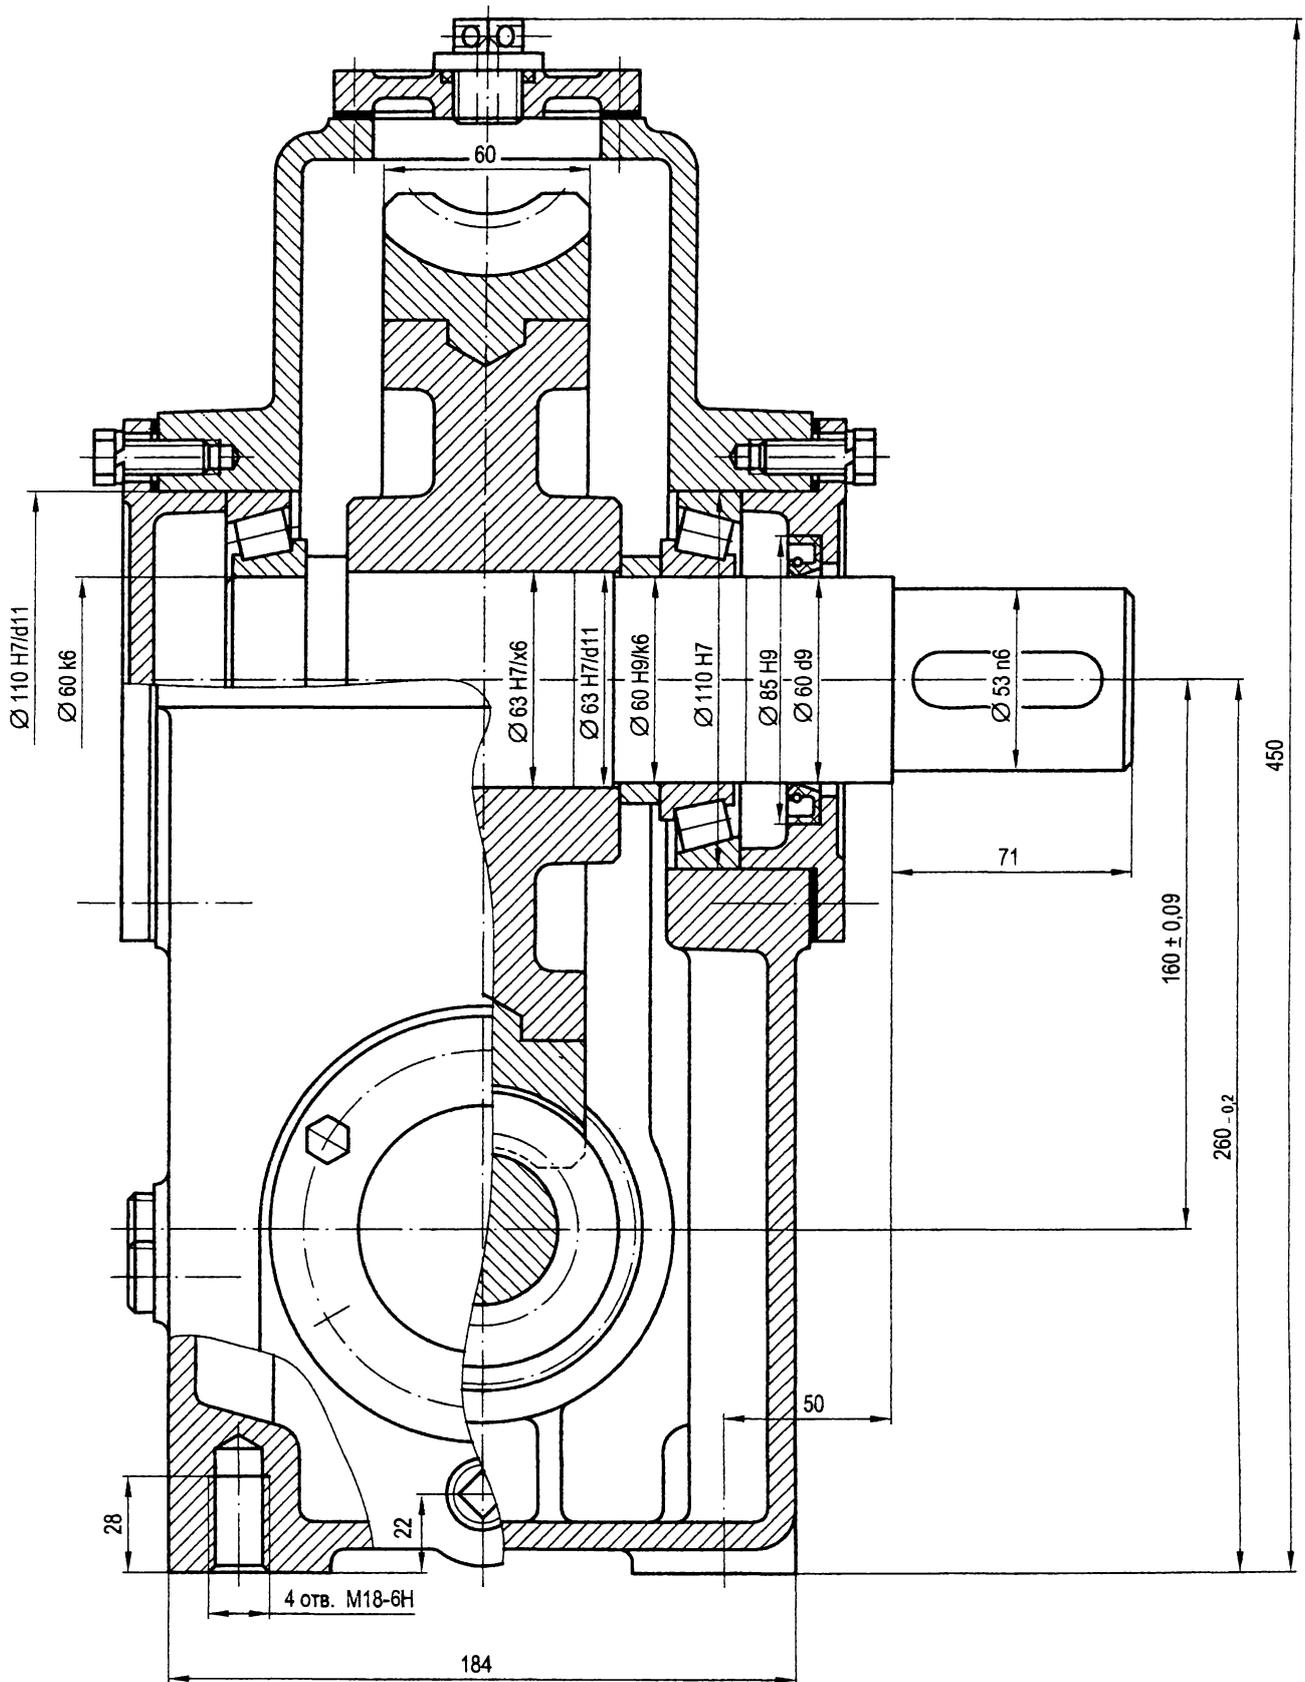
Тихоходный (выходной) вал редуктора с червячной передачей
